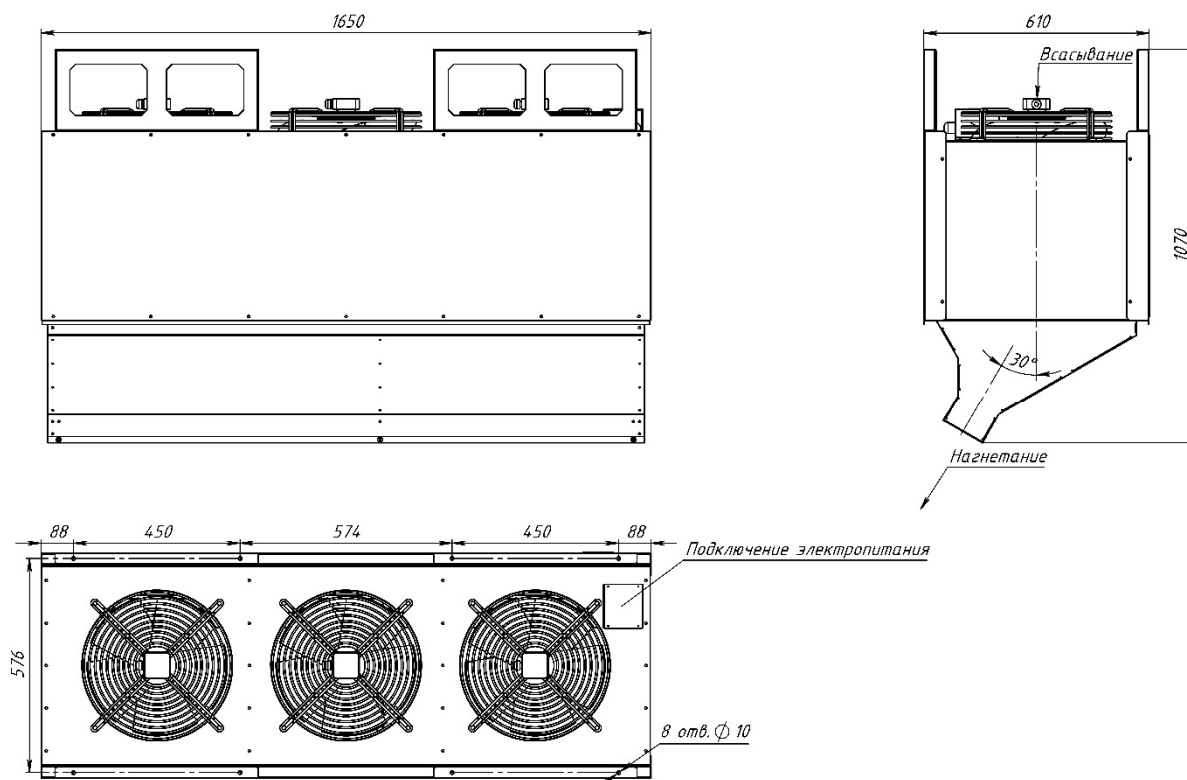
Габаритные и присоединительные размеры SA1 7500 Z (левое исполнение)
